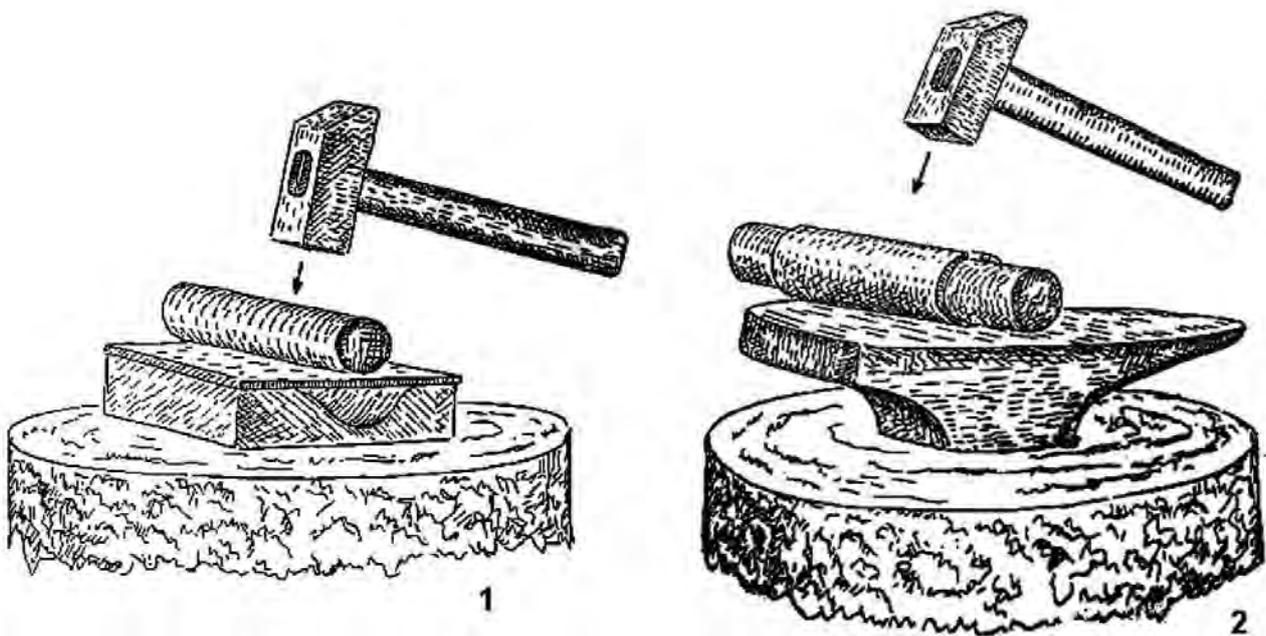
Эксперимент по изготовлению реплики цилиндрического пружинного замка типа В (по типологии Б.А. Колчина). Процесс изготовления заготовки корпуса цилиндрического замка на специальной оправке.
